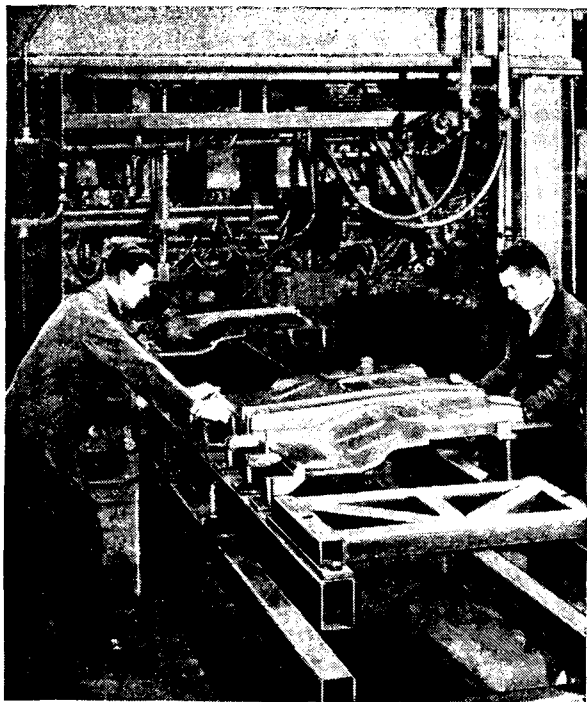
Многоэлектродная многопозиционная машина для сварки панелей пола.
